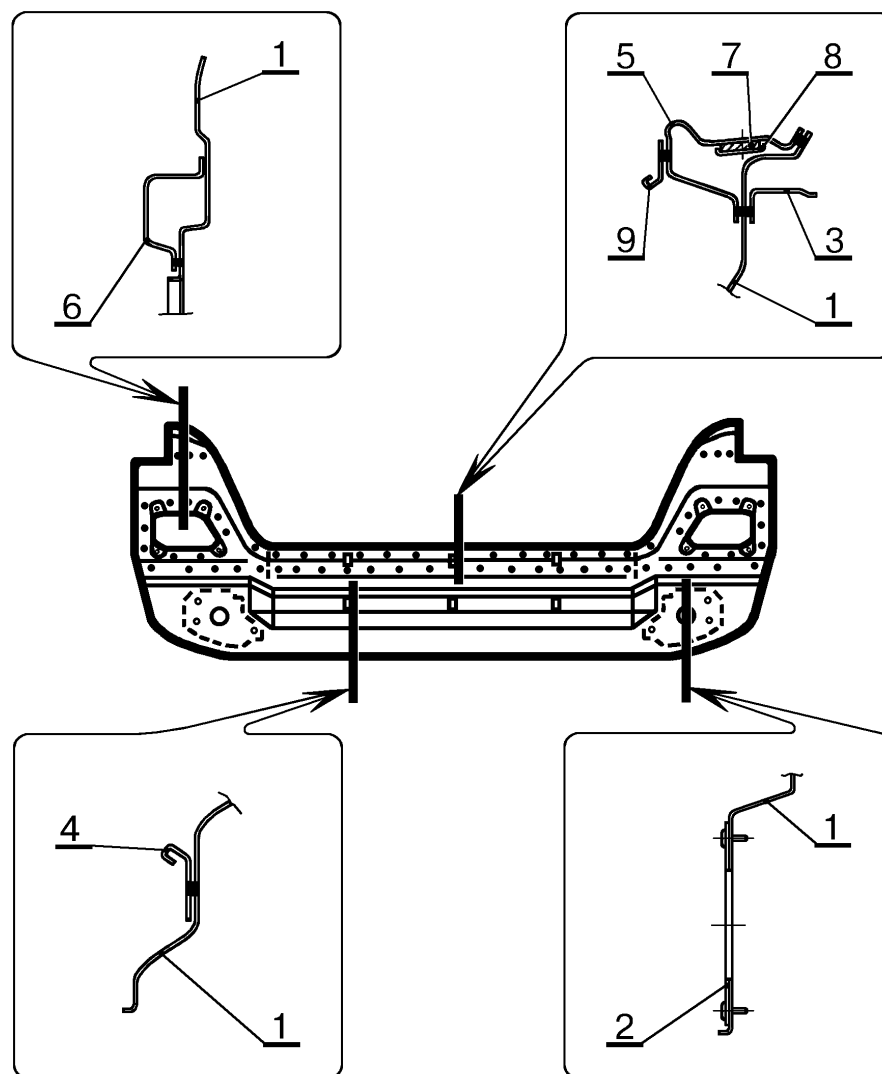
Детали панели 2115-5601080 задка в сборе. Номера и наименования деталей, количество сварочных точек приведены в таблице 13.
